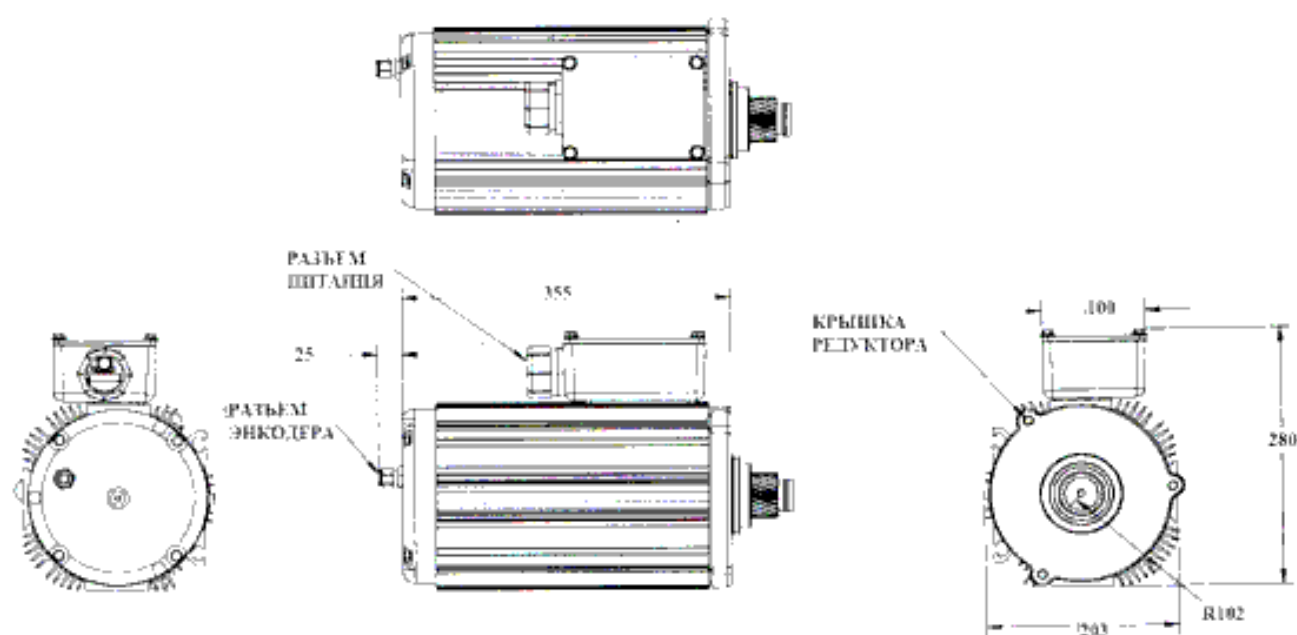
Габаритный чертеж электродвигателя АС24
